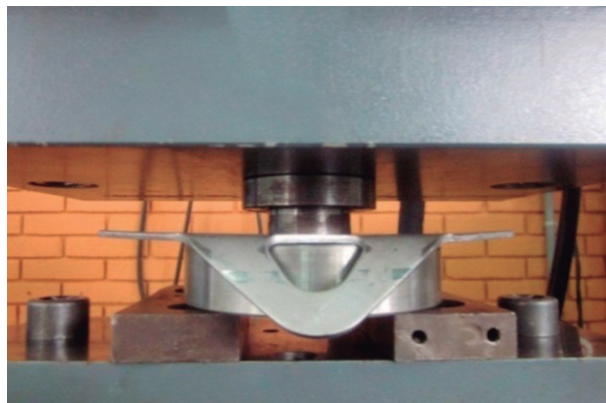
Ensayo de tracción sobre la placa refilada.
